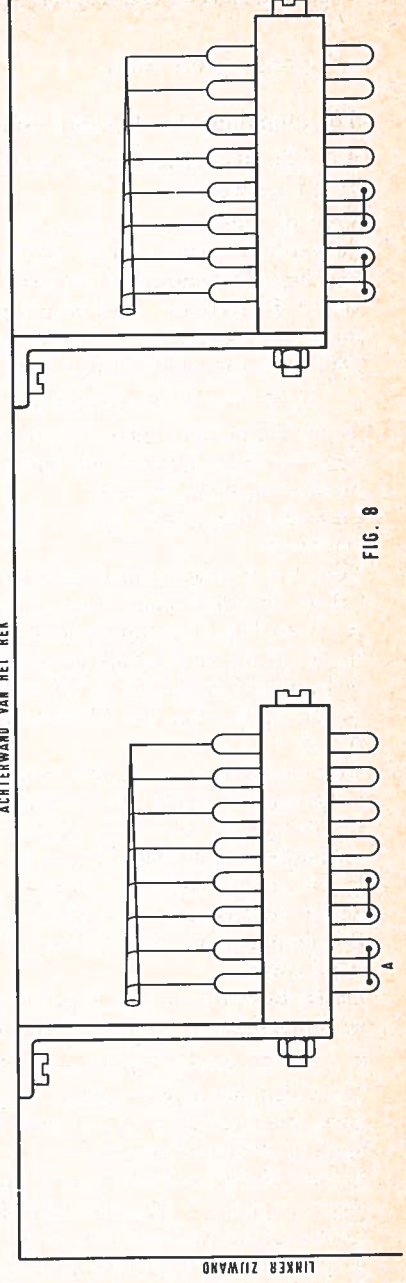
toont het bovenaanzicht hiervan, waaruit blijkt, dat de blokjes loodrecht op de achterwand aangebracht zijn. Ze staan 100 mm uit elkaar, terwijl de draadtampjes 50 mm lang zijn. Tussen deze draadboompjes en de rechts ervan gelegen soldeerstift blijft een ruimte van ca. 25 mm over.
